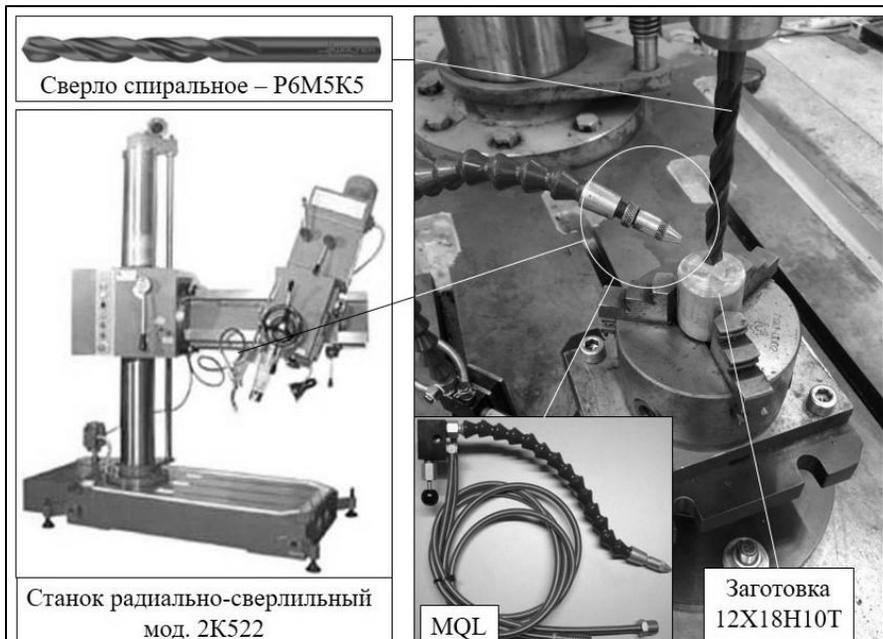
Экспериментальный стенд для исследования влияния приработки на стойкость режущего инструмента при сверлении
